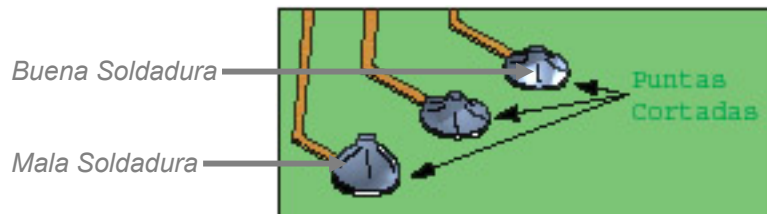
Buena vs Mala Soldadura. Una soldadura aceptable es de forma cónica.
